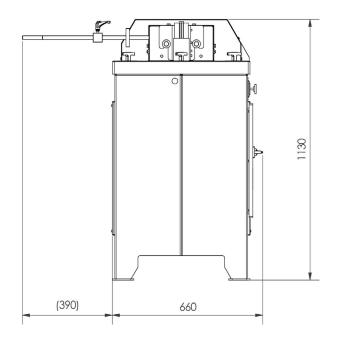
Dimensions extérieures de la Presse plieuse horizontale.
